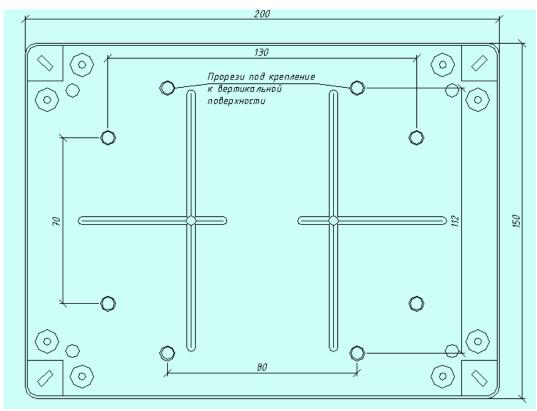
Габаритные и установочные размеры блока «БАКС-10М»
